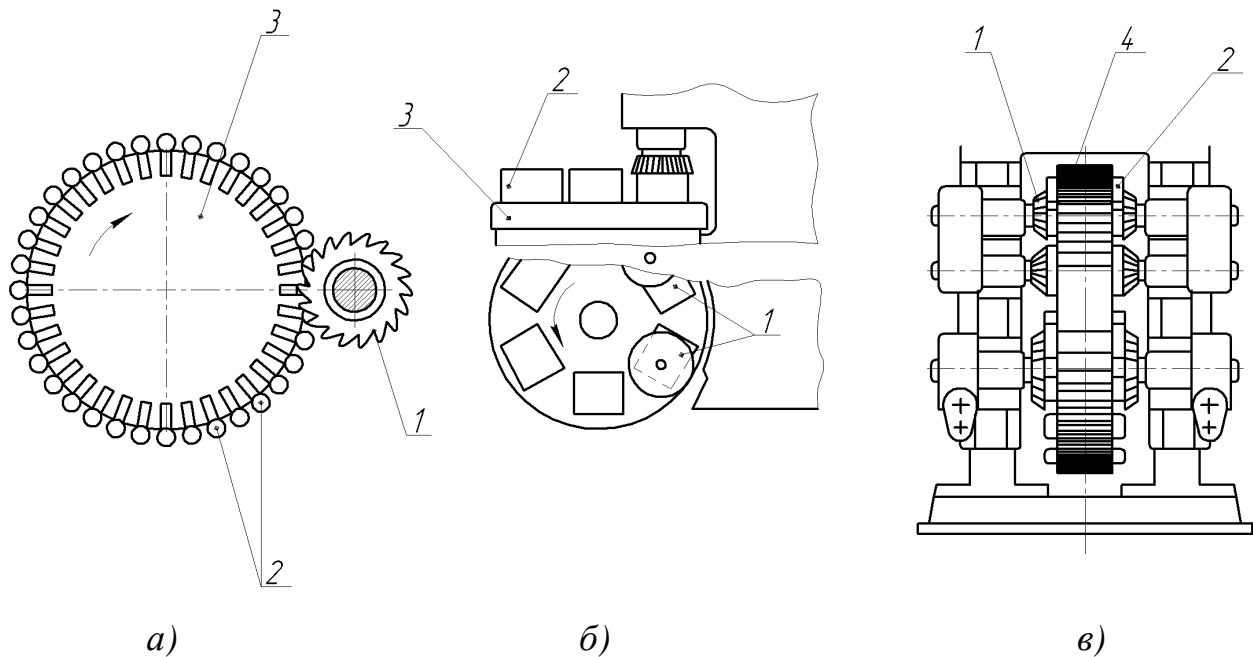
Розміщення заготовок при обробленні на карусельно-фрезерному верстаті з одним шпинделем (а); карусельно-фрезерному верстаті з двома шпинделями (б); барабанно-фрезерному верстаті (в):
